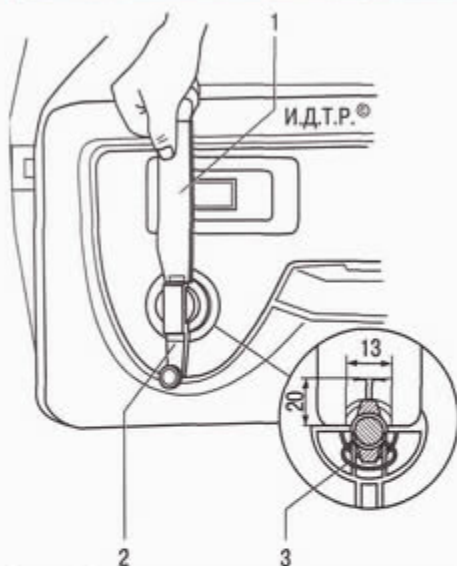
Снятие ручки привода стеклоподъемника: 1 — приспособление; 2 — ручка стеклоподъемника; 3 — стопорная пружина
